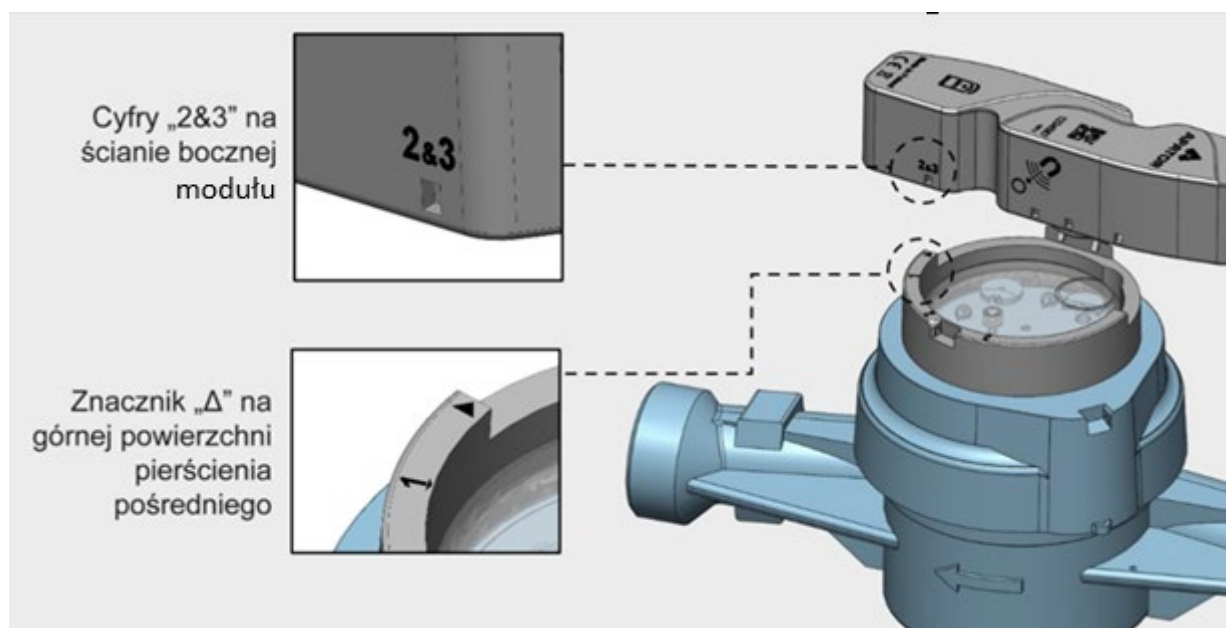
Pozycjonowanie pierścienia blokującego przed montażem na pierścieniu pośrednim.
